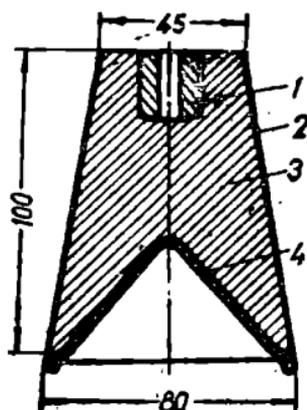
Кумулятивный накладной заряд для дробления негабарита ИРН = 400:
